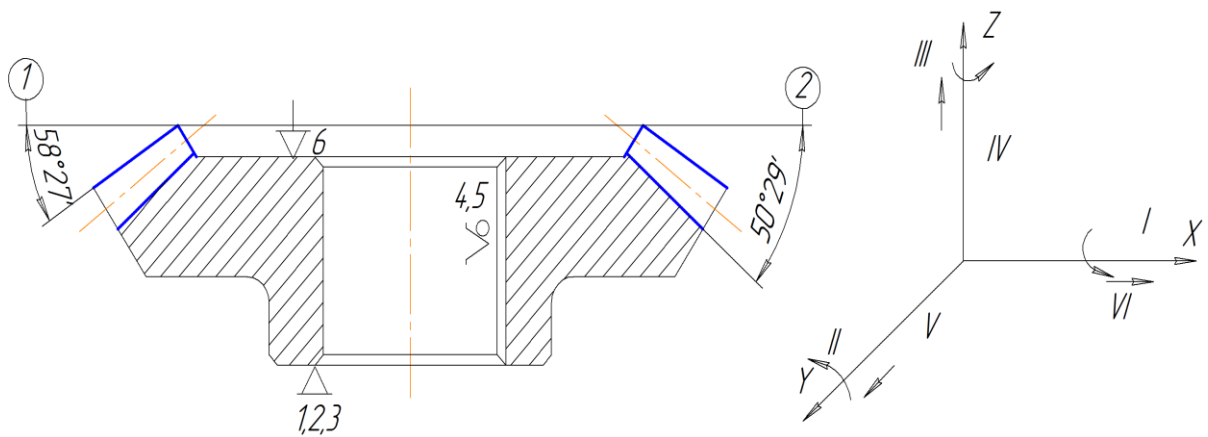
Схема базування та закріплення заготовки на операції 025
